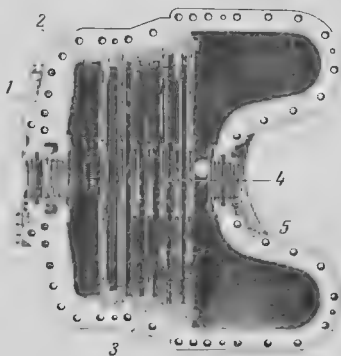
Верхняя часть корпуса небольшой активной турбины (вид снизу).
